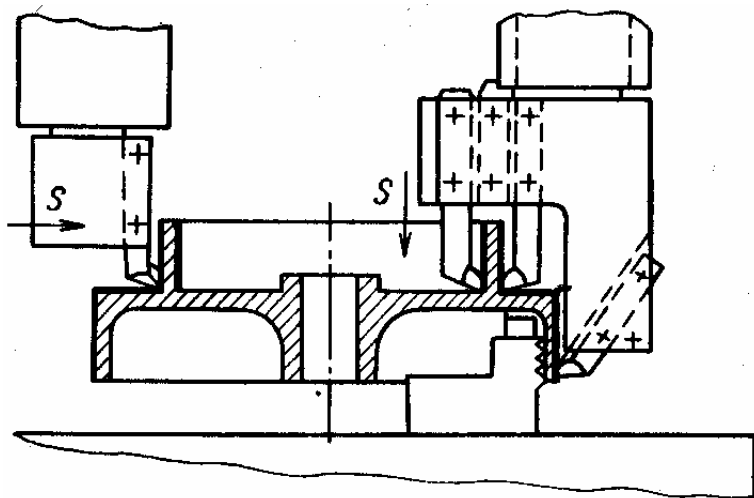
Схема багатопрограмної обробки великогабаритної заготовки
